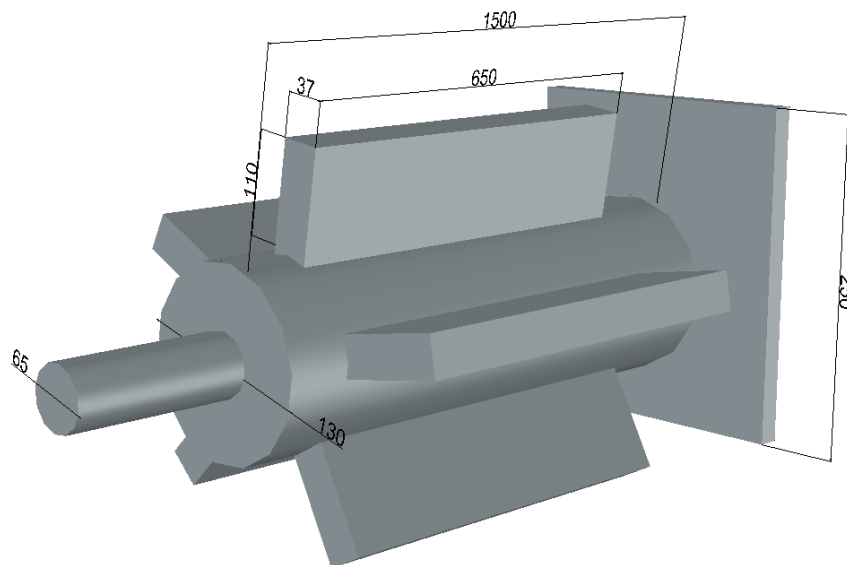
Esquema de armado propuesto de rotor con aletas y placa base
